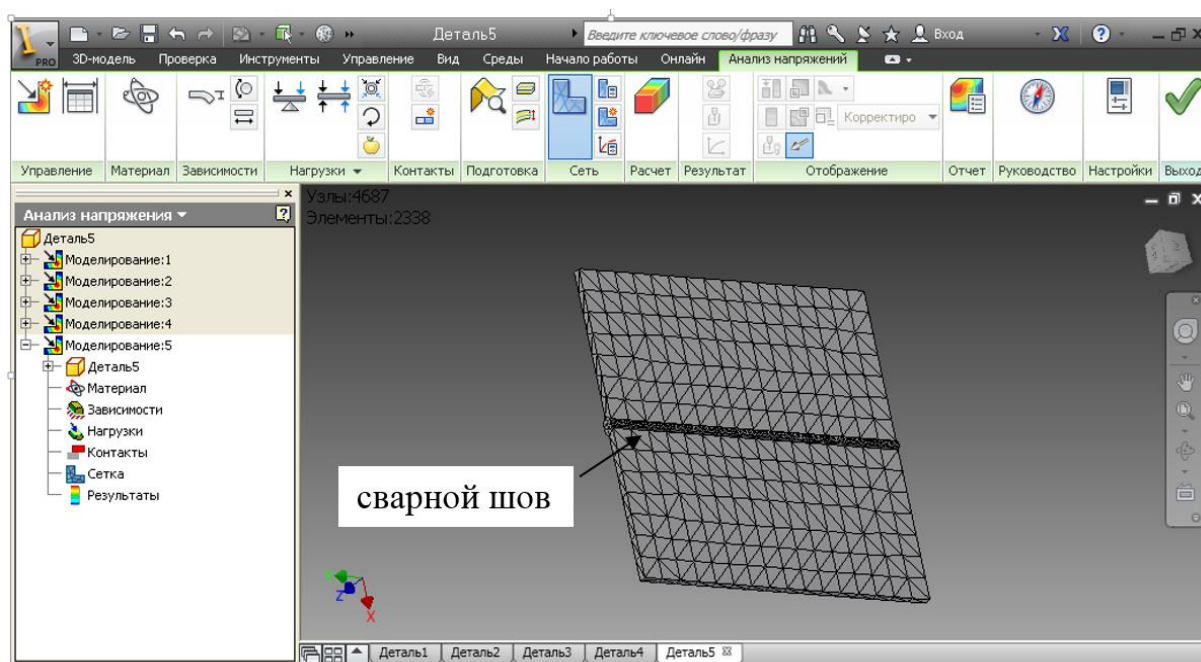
Конечноэлементная модель сварной конструкции из 2-х пластин
